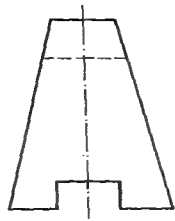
Dibujar el perfil de un objeto representado mediante alzado y planta.
